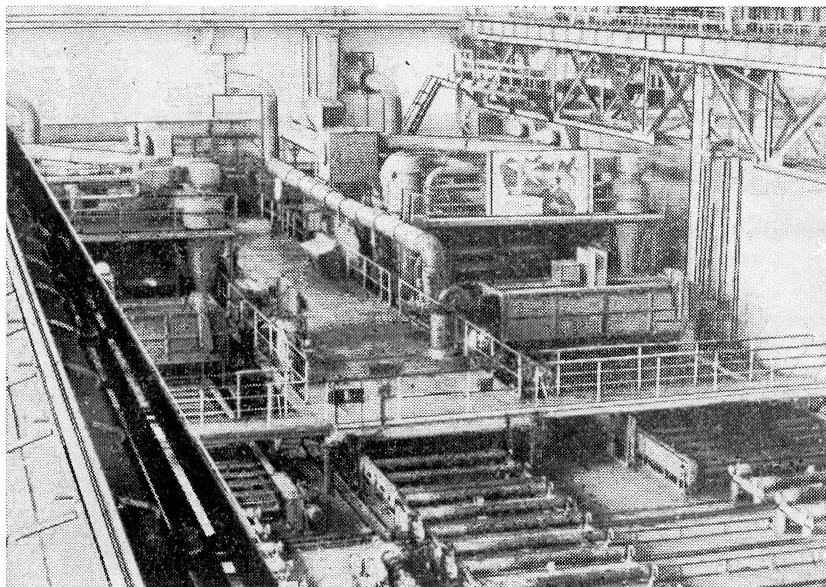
Линия очистки и грунтовки листового и профильного проката.
